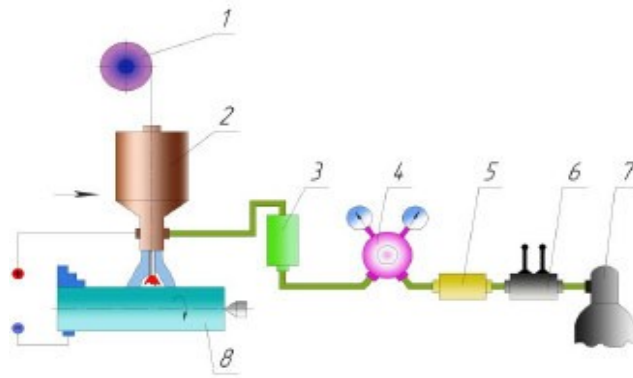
Схема установки для дугового наплавлення в середовищі 32:
